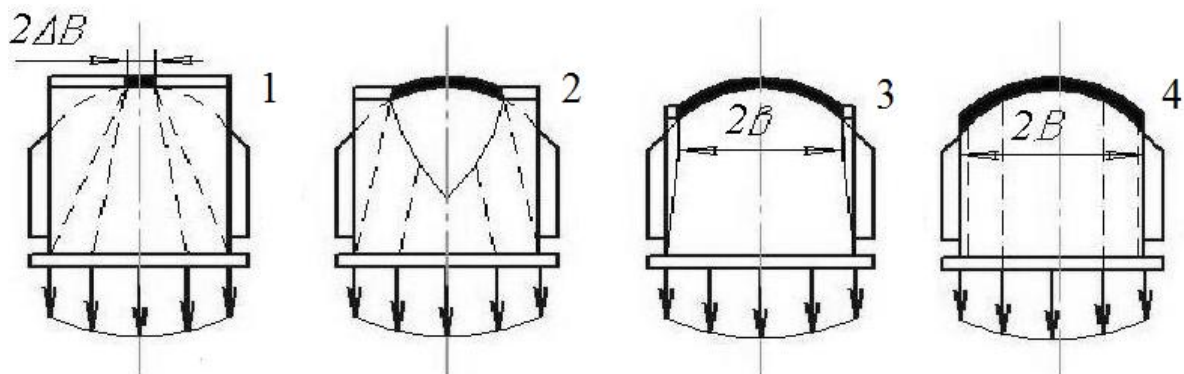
Предварительная обтяжка оболочки двояковыпуклой формы после полного оборачивания обтяжного пуансона листовой заготовкой на угол α_k
